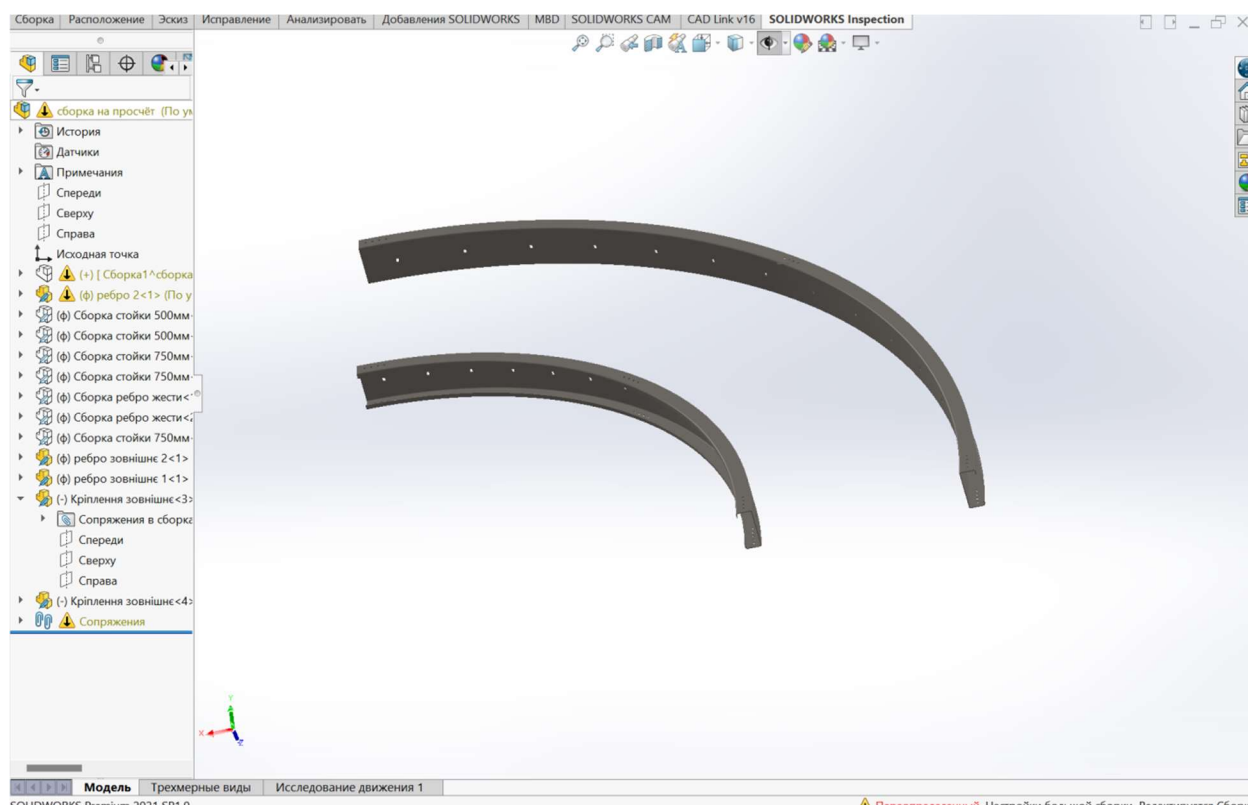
Корпус для кріплення роликів, та стійок
